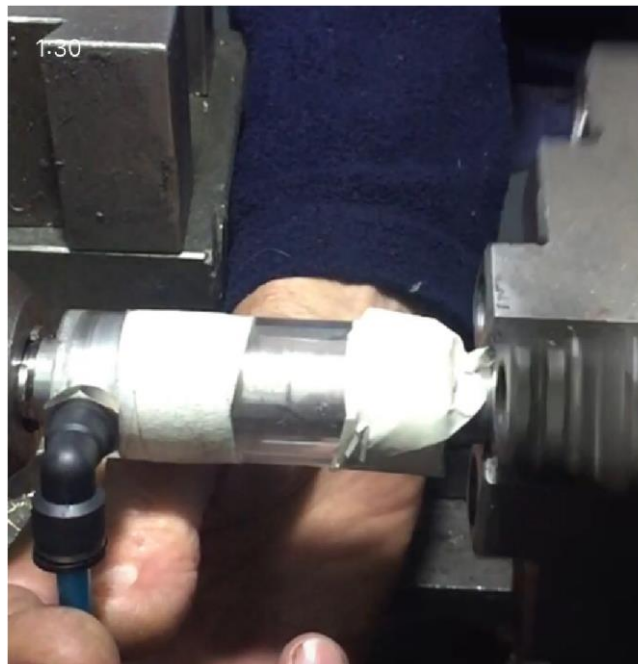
Sistema puesto a punto para dar inicio a la soldadura.
